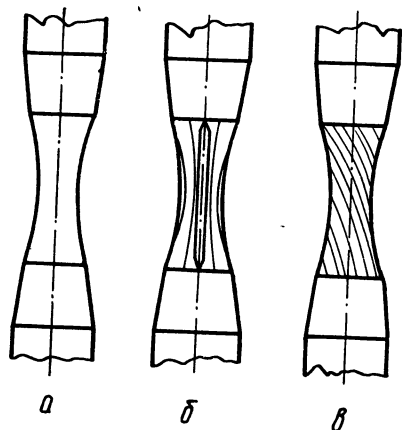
Конструкция литых образцов с различной формой поверхности для определения прочности на разрыв: а — гладкая; б — продольнорифленая; в — корифленая.
